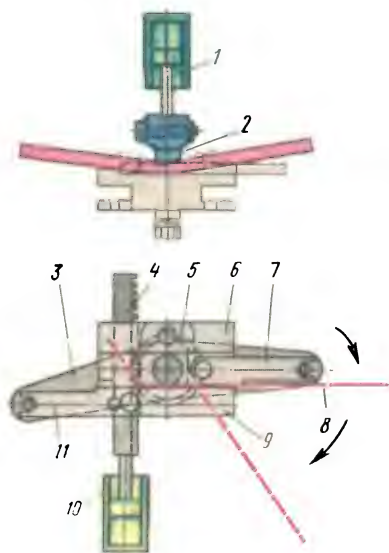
Пневматический станок для изгибания лобовых частей стержней обмотки ротора
